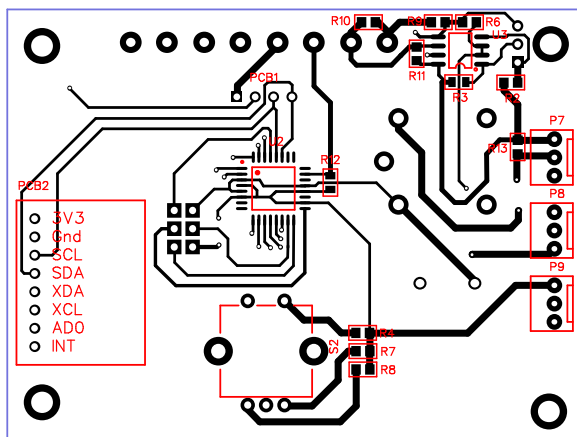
Монтажна схема верхнього шару друкованої плати
